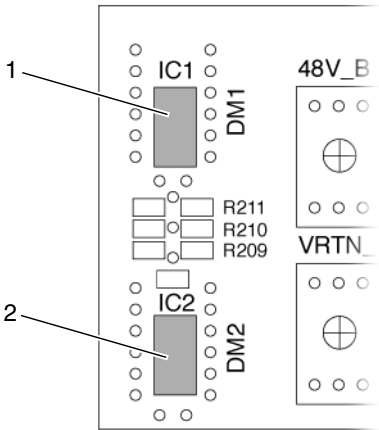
Posizione delle SEEPROM sul midplane (vista posteriore)
